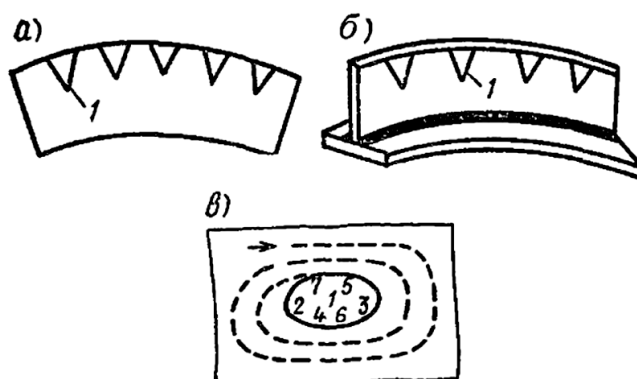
Термическое исправление деформации: а — серповидность листа; б — изгиба сварного тавра; в — хлопуна
